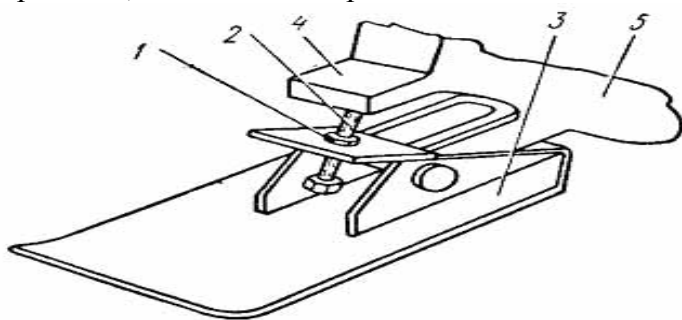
Схема установки плуга ПКЛ-70 на глубину пахоты: 1 — контргайка, 2 — регулировочный болт, 3 — опорная пята, 4 — упор, 5 — корпус плуга
